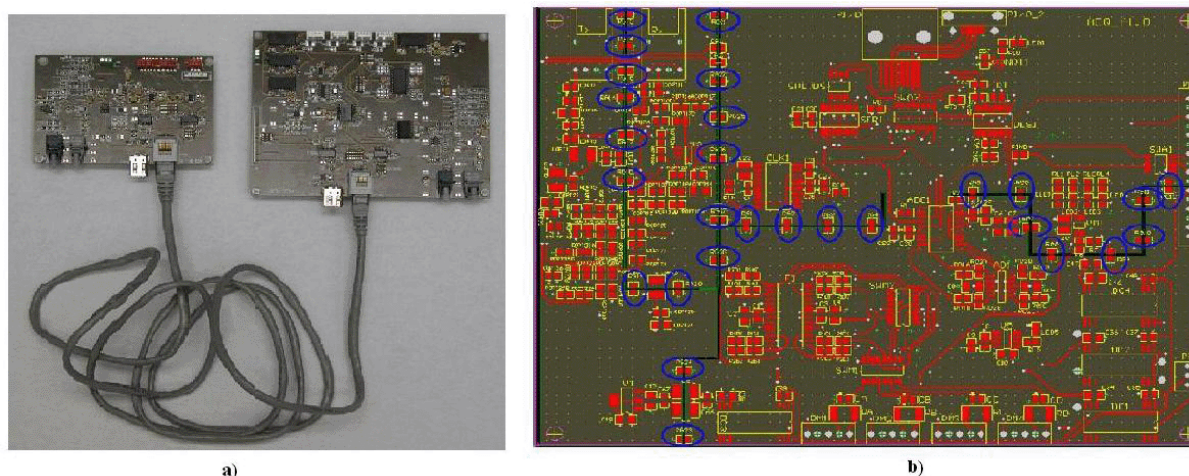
a) Realizzazione delle schede; b) layout delle PCB
